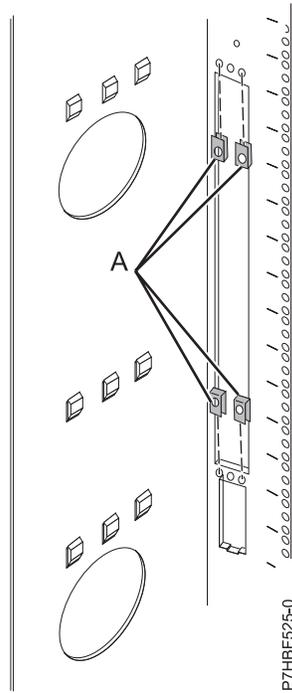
Klemmmuttern an Rackbefestigungsflanschen anbringen
